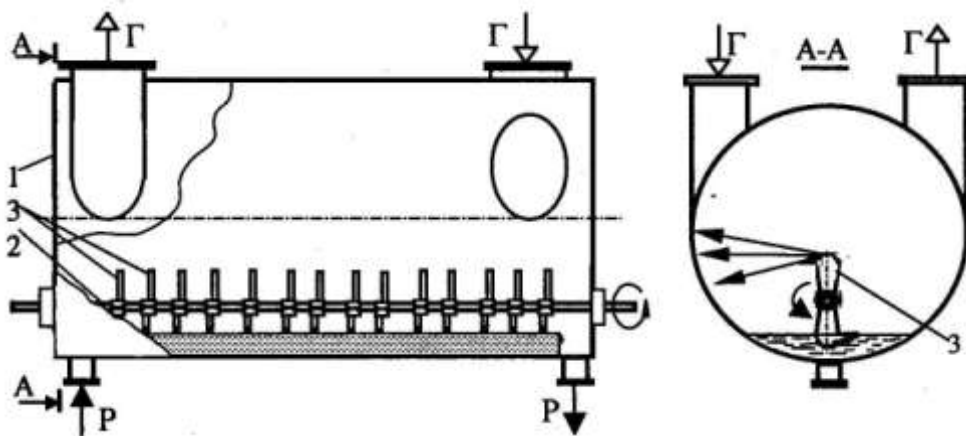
Скруберна камера з механічними ковшоподібними розбризувачами: 1 – корпус; 2 – вал; 3 – ковшоподібні розбризувачі
